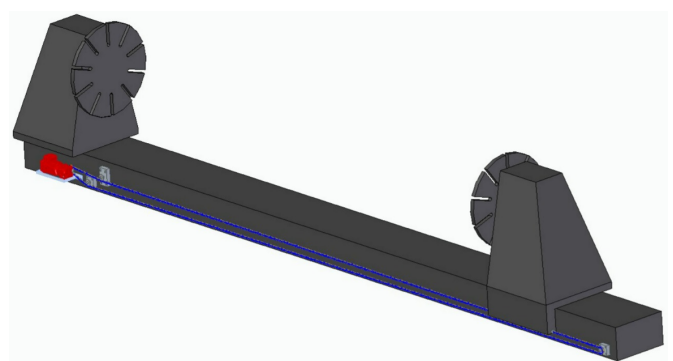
Desenho 3D da célula de soldagem. Fonte: Autoria própria (2026).
